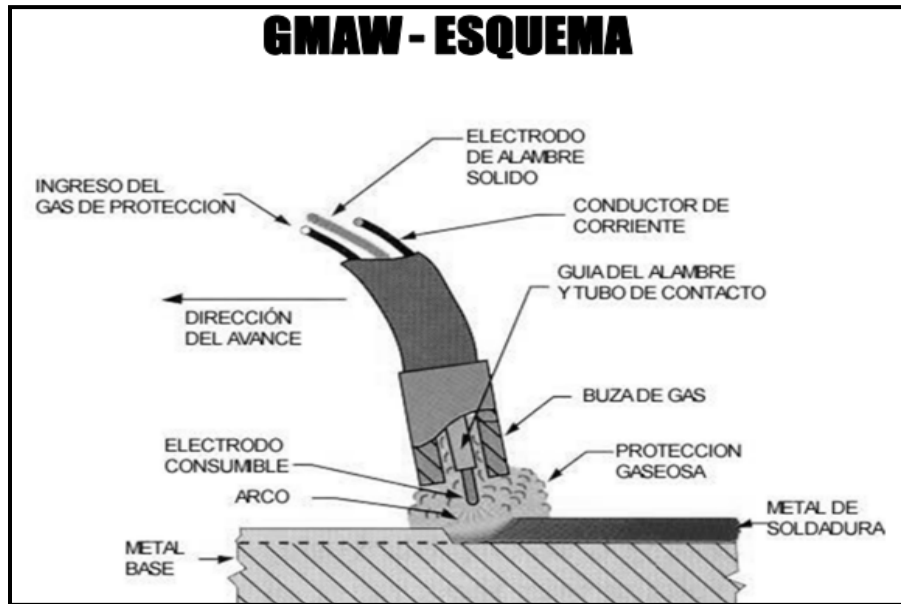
Procesos de soldadura (GMAW)
